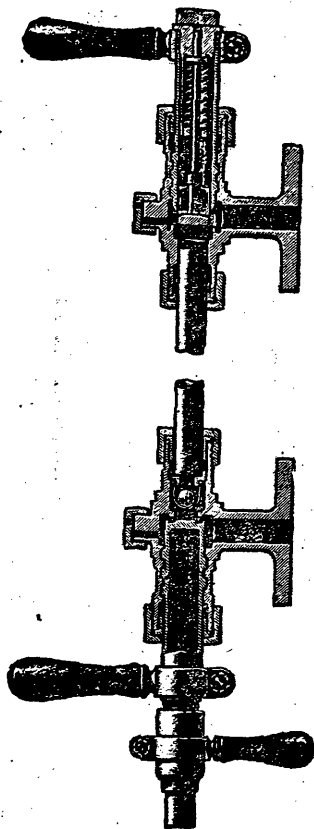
Cierre automático para tubo indicador de nivel de agua, sistema Weinmann y Lange.
